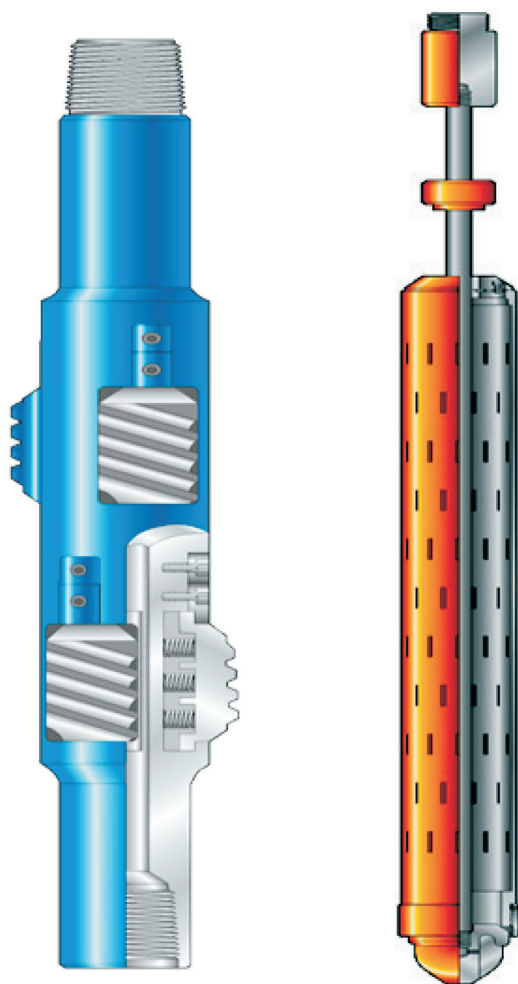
Скребок для обсадных труб (слева); спускаемый на канате шламометаллоуловитель и калибрующее кольцо (справа)
